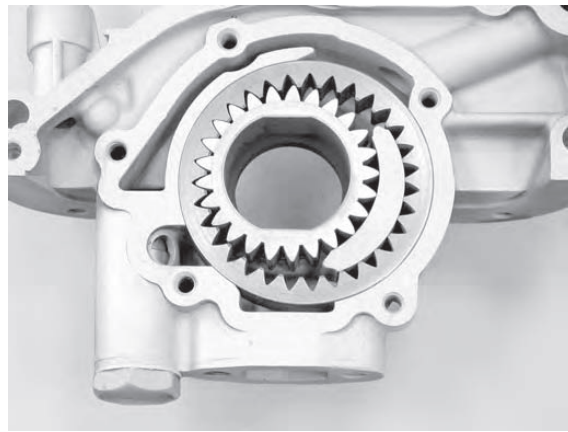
Bomba de engrenagem interna. Adaptado de [16].
